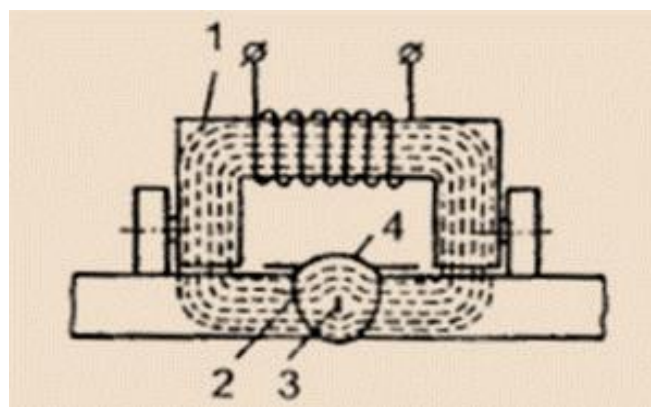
Проверка качества сварных швов магнитной дефектоскопией:
